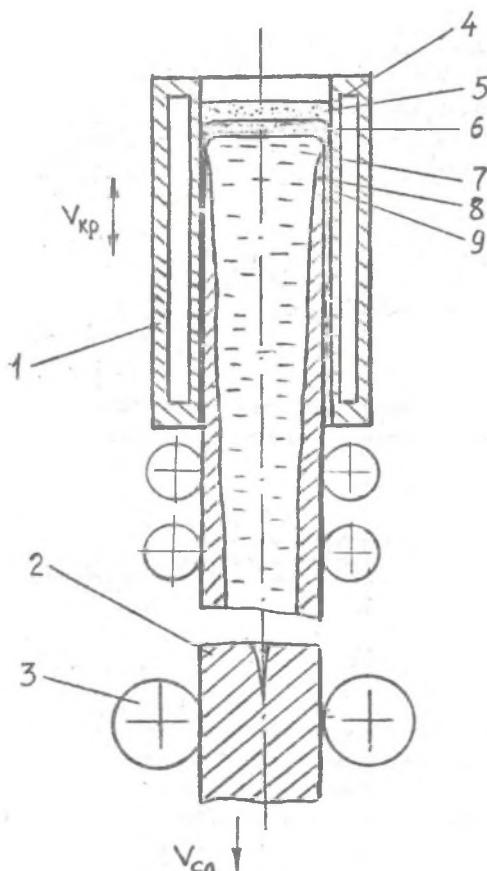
Схема непрерывного литья заготовок; 1-кристаллизатор, 2-непрерывный слиток, 3-тянущие валки, 4-водоохлаждаемые рабочие стени кристаллизатора, 5-сырьи слой шлакообразующей смеси, 6-шлаковый расплав, 7-жидкий металл, 8-затвердевающая корка слитка, 9-смазочные слои между коркой и рабочими стенками.
